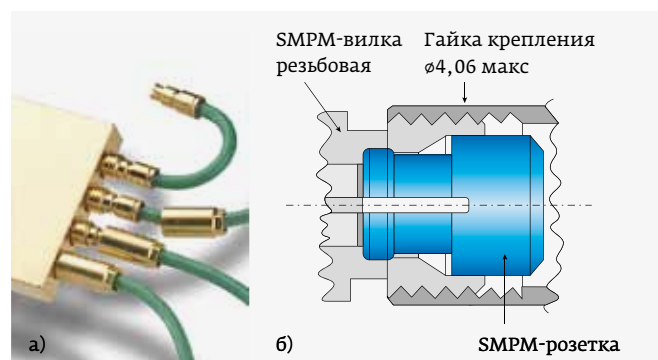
Соединитель SMPM-T: а – внешний вид; б – конструкция
